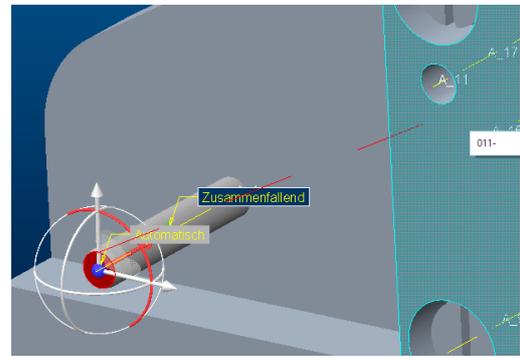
Stirnfläche des Stiftes auf Bauteilfläche
